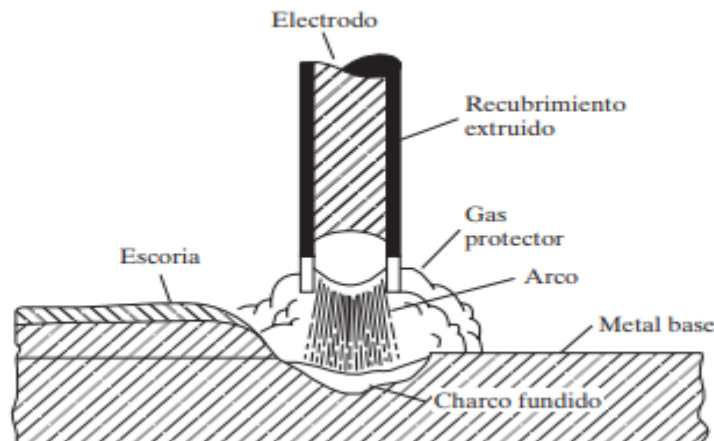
Elementos involucrados en la soldadura de arco metálico protegido (SMAW), [16].
